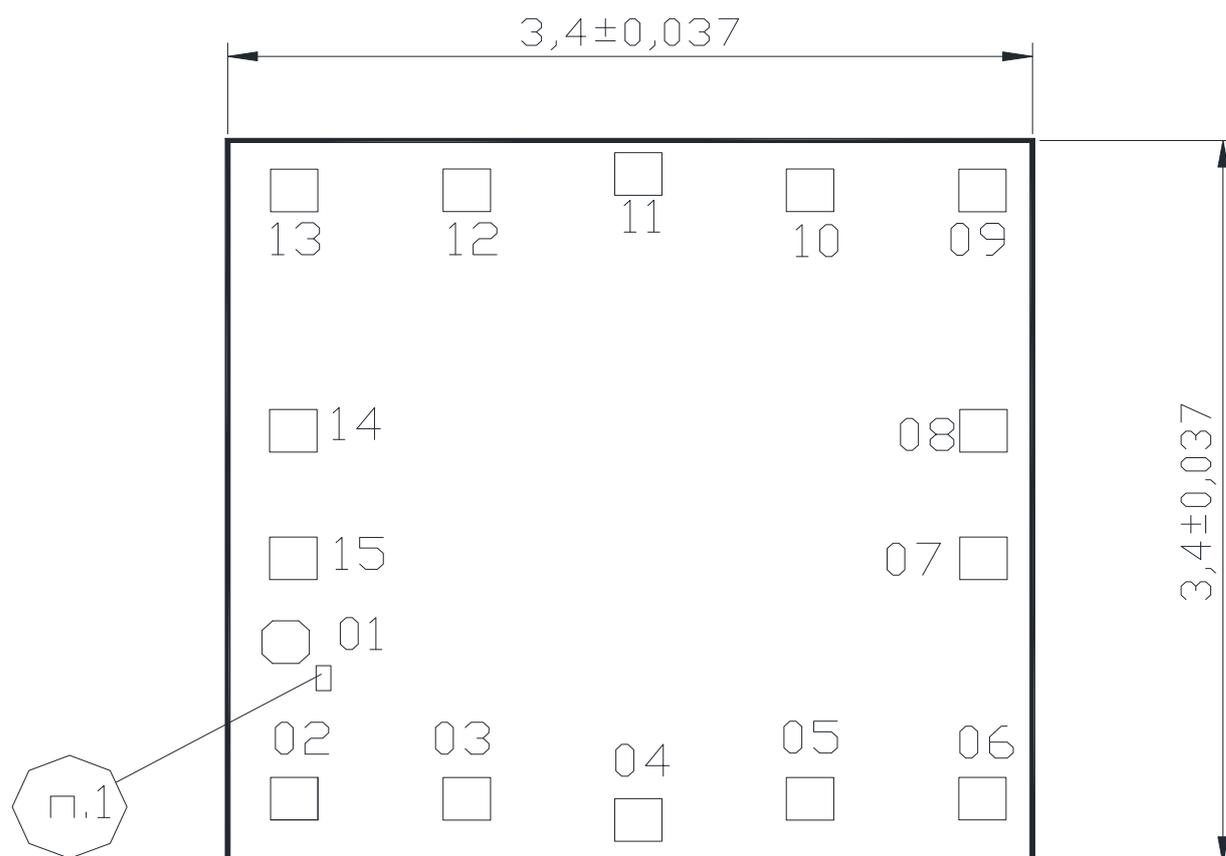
Габаритные размеры корпуса H04.16-2B
